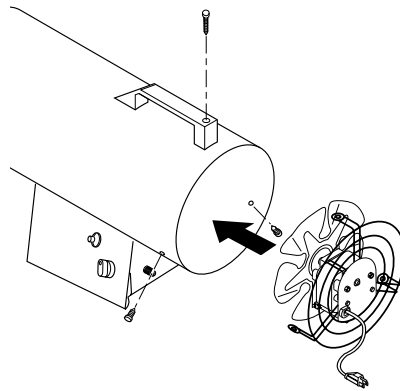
Remise en place du moteur et de la grille du ventilateur
